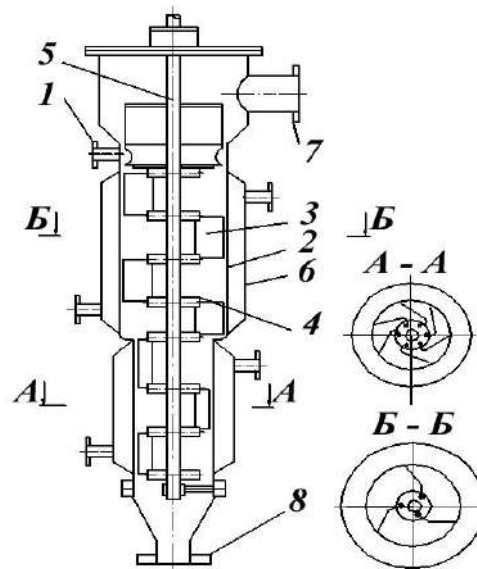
Роторний випарник зі ступінчастим корпусом:
